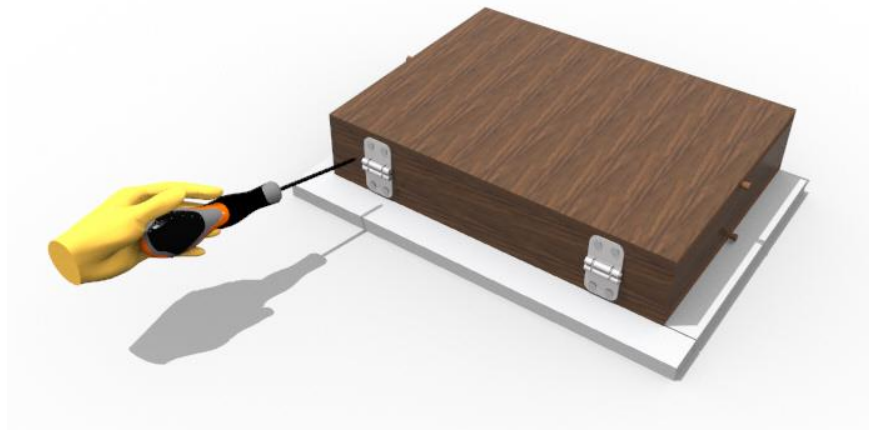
Ensamblaje de los cierres mediante tornillería
